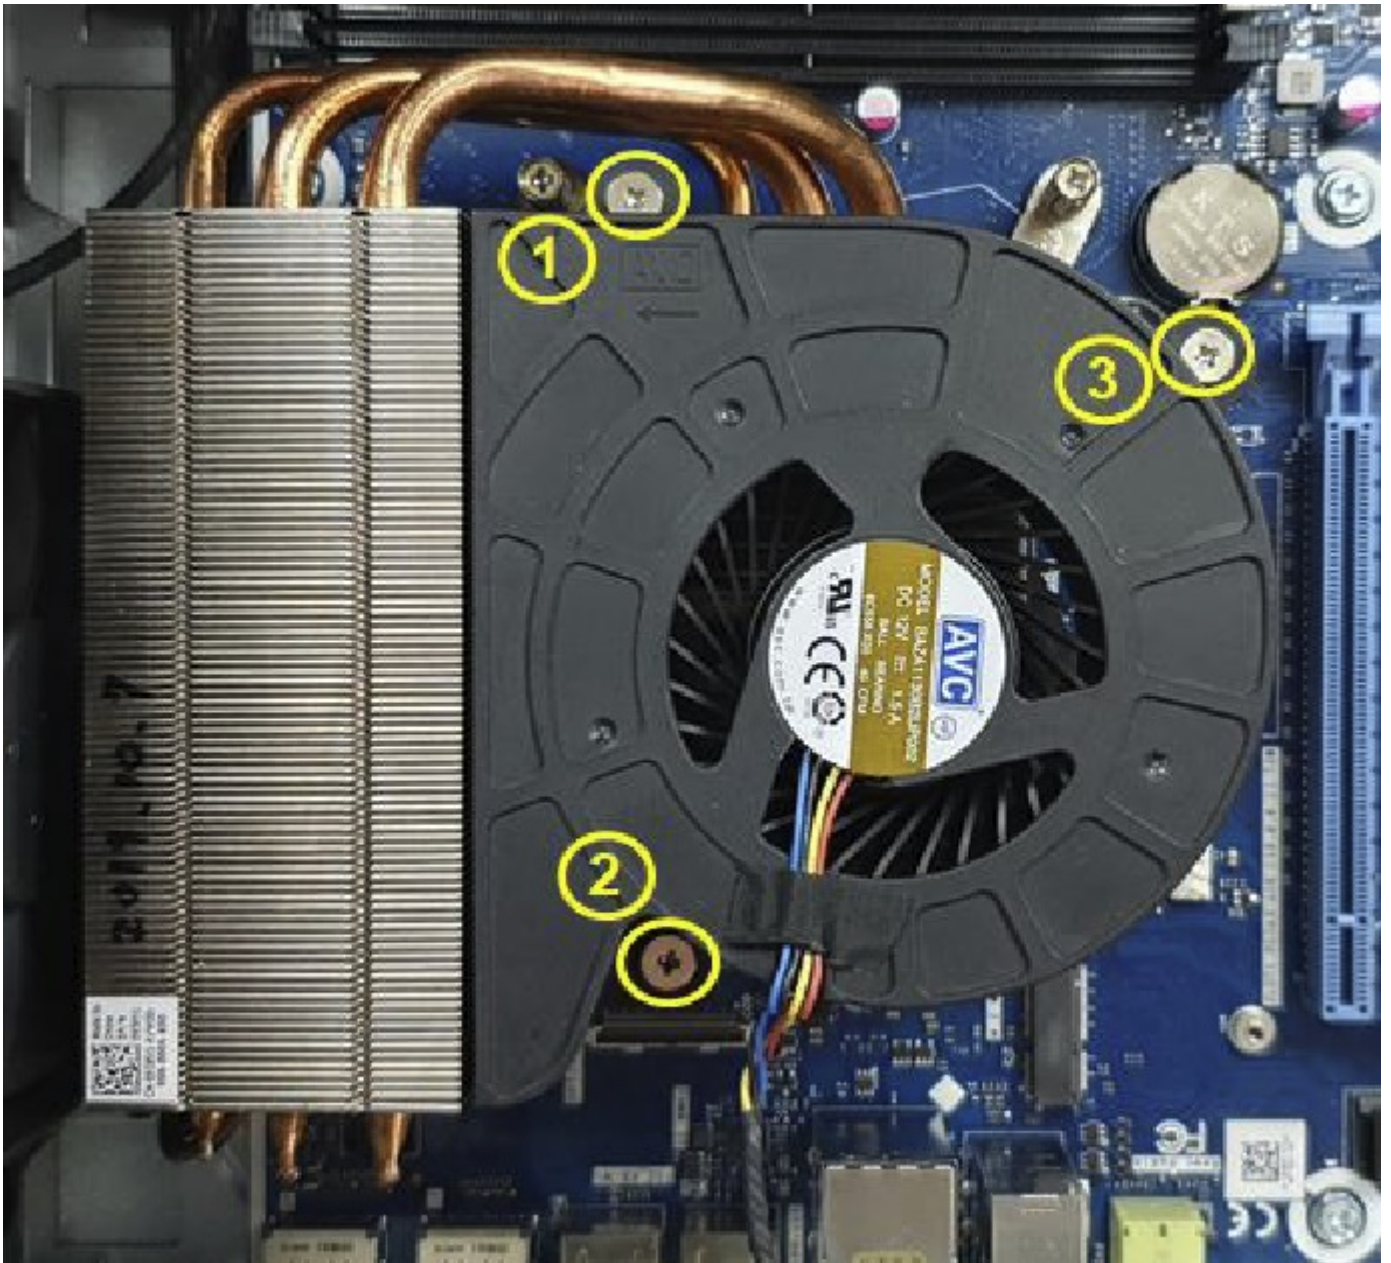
Conjunto do dissipador de calor - CPU de 65 W ou 80 W
